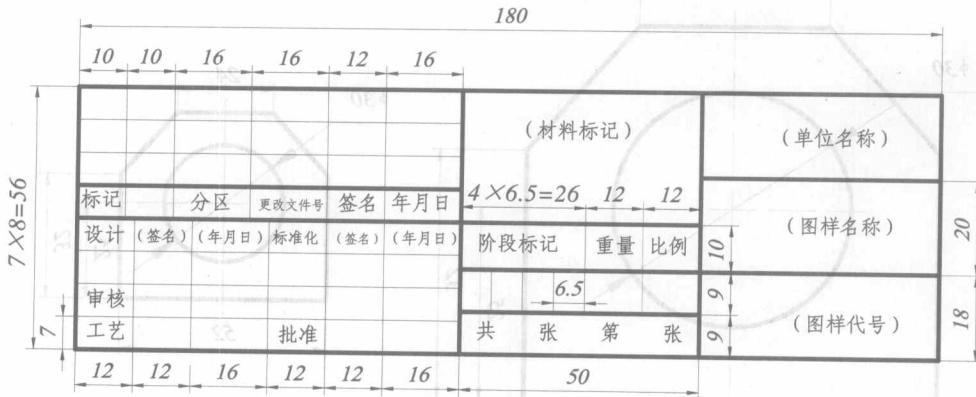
标准规定的标题栏规格与尺寸 (单位: mm)
